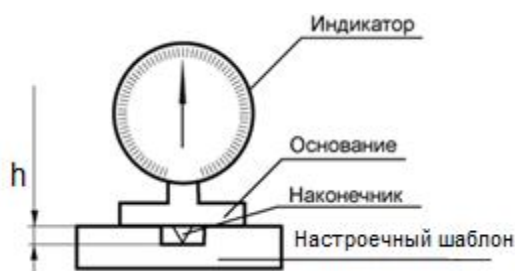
Схема настройки прибора для измерения высоты профиля резьбы
